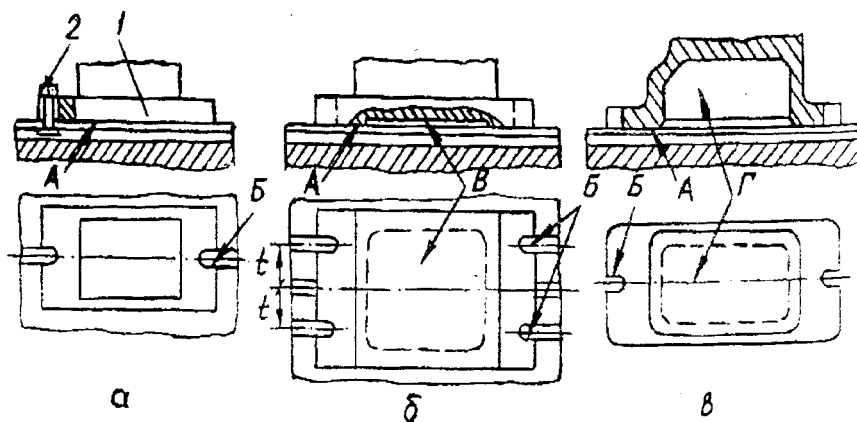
Посадочные поверхности корпусов фрезерных приспособлений
